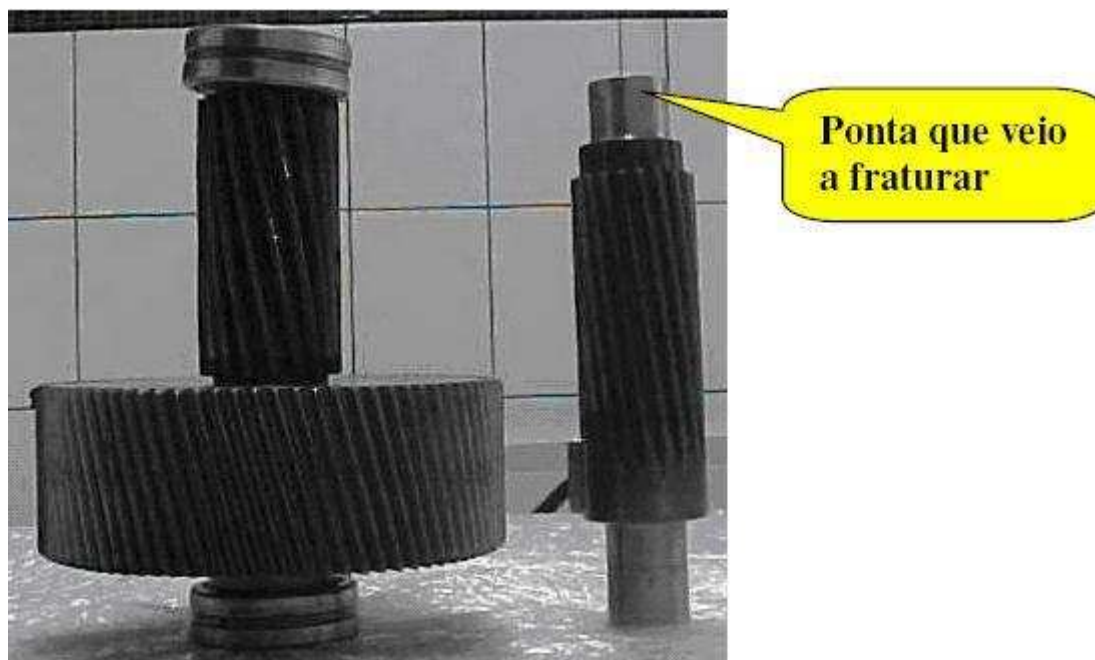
Eixo antes da falha. Montado em rolamentos e engrenagem e desmontado, respectivamente.
